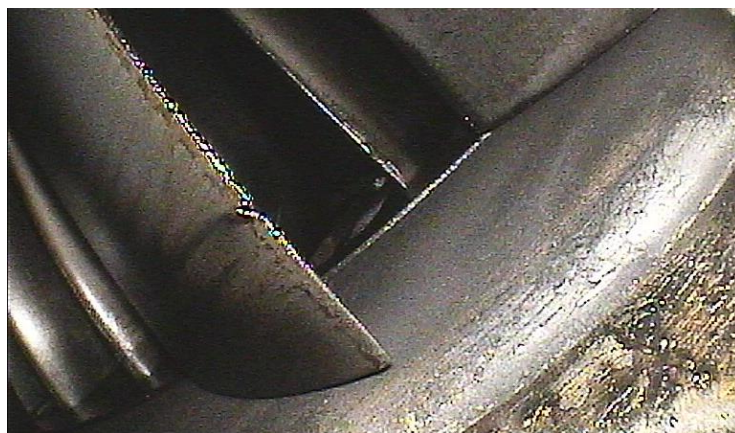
Забоина на входной кромке рабочей лопатки 6 ступени компрессора до 1 мм
